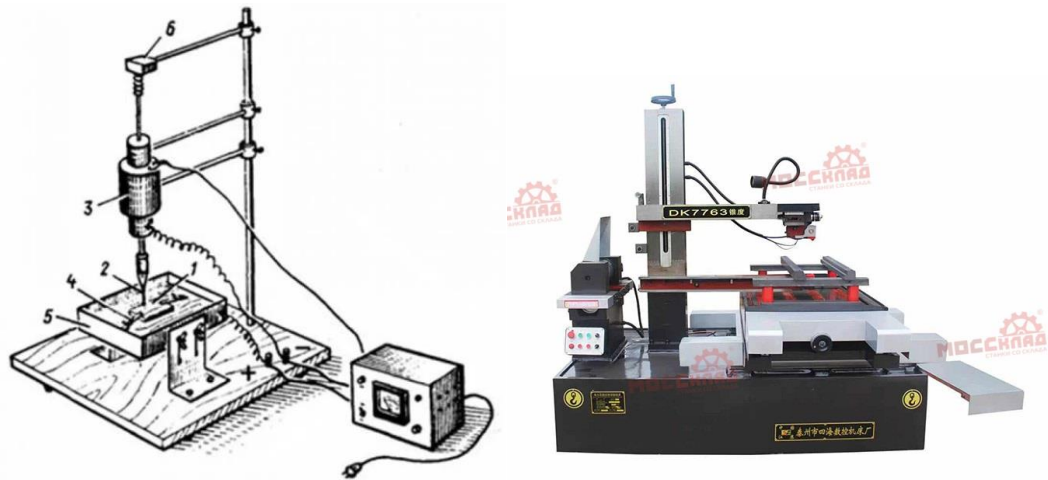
Електроерозійний верстат: 1 – електрод; 2 – гвинт фіксації електрода в направляючій втулці; 3 – зажим плюсового контакту; 4 – направляюча втулка; 5 – корпус з фторопласта; 6 – отвір для подачі змазки; 7 – станина.
